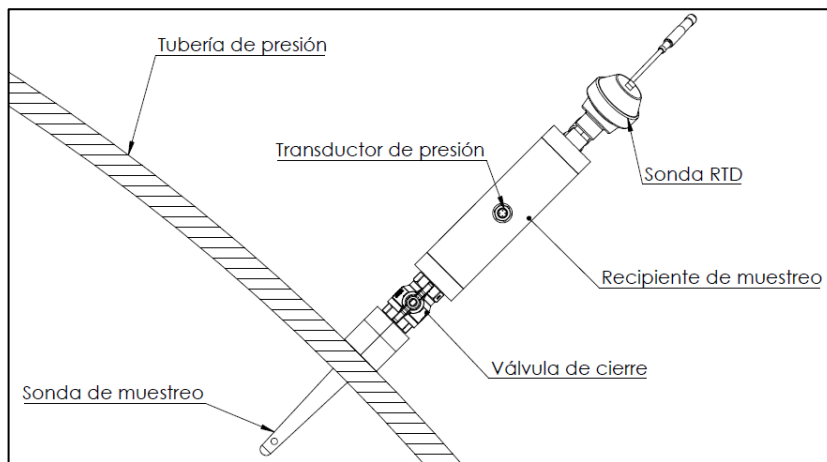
Dispositivo de muestreo montado en la tubería de presión.
